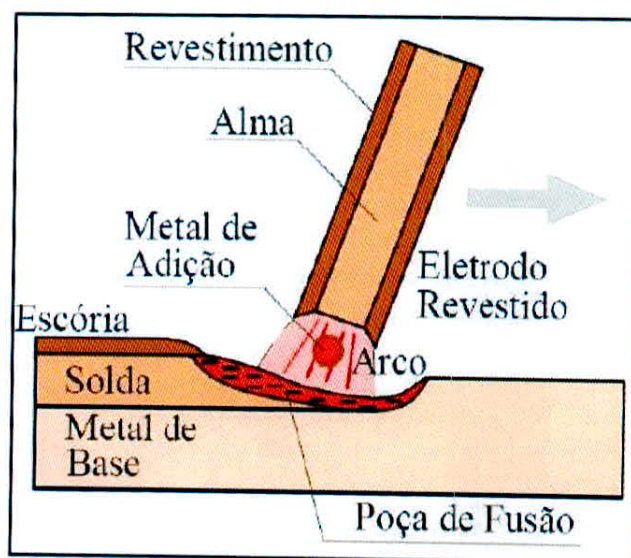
Esquema de uma soldagem com eletrodo revestido.
